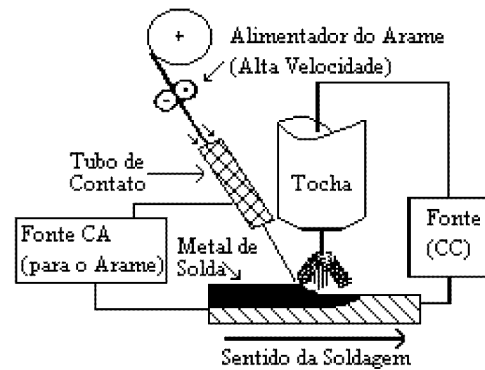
Soldagem TIG com “Arame Quente”.
